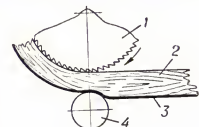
Схема гнутья древесины с одновременным прессованием: 1 — шаблон; 2 — заготовка; 3 — шина; 4 — прессующий ролик.
